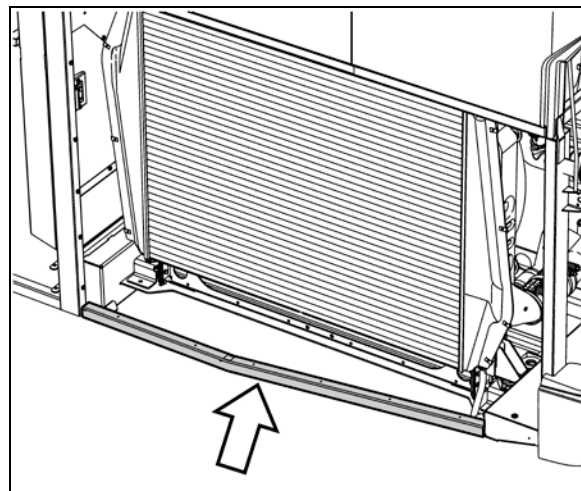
PROTECTEUR DU TUBE DE L'ENSEMBLE RADIATEUR INFÉRIEUR
